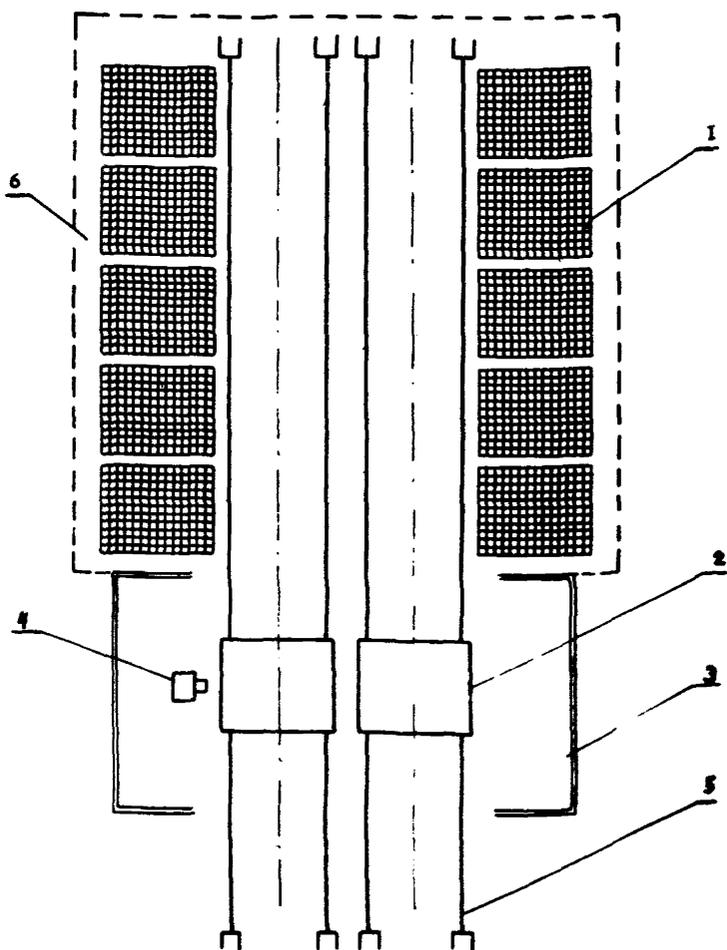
Схема арматурного цеха с подвижными кондукторами: 1-штабеля готовой арматурной сетки; 2-подвижные кондукторы; 3-арматурный цех; 4-подвесные вешки для контактной сварки К-260; 5-рельсы; 6-склад готовой продукции
